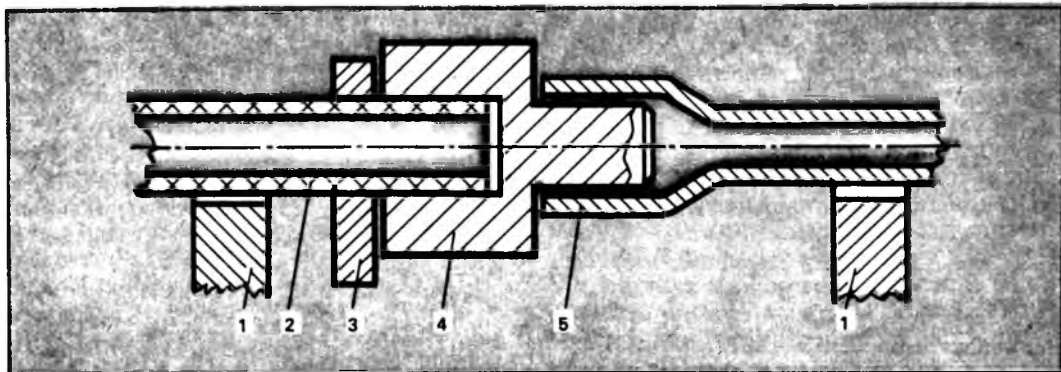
Металлическая оправка для образования раструба в пластмассовой трубе: 1 — корпус, 2 — рукоятка, 3 — направляющая и формирующая часть
